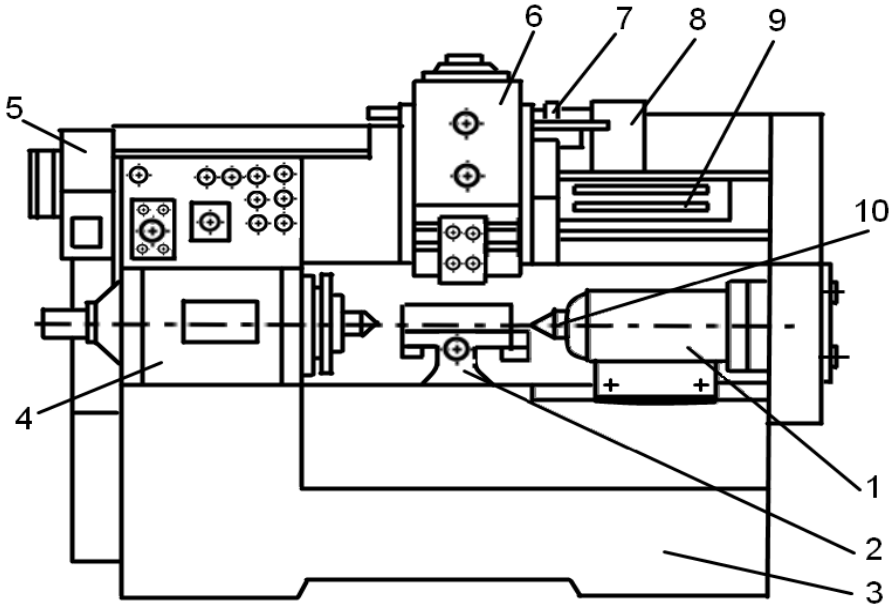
Загальний вигляд багаторіздевого токарного напівавтомата
